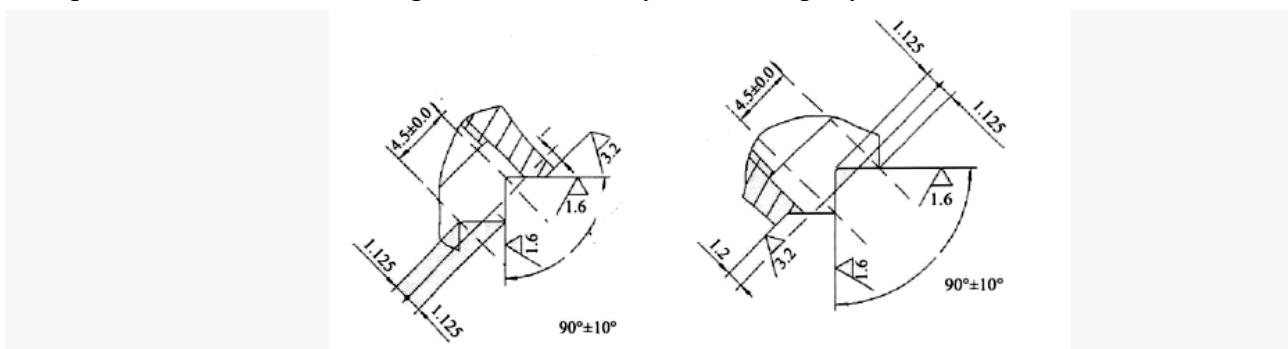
Схема профиля зуба поверхностей соединения стержень – головка
